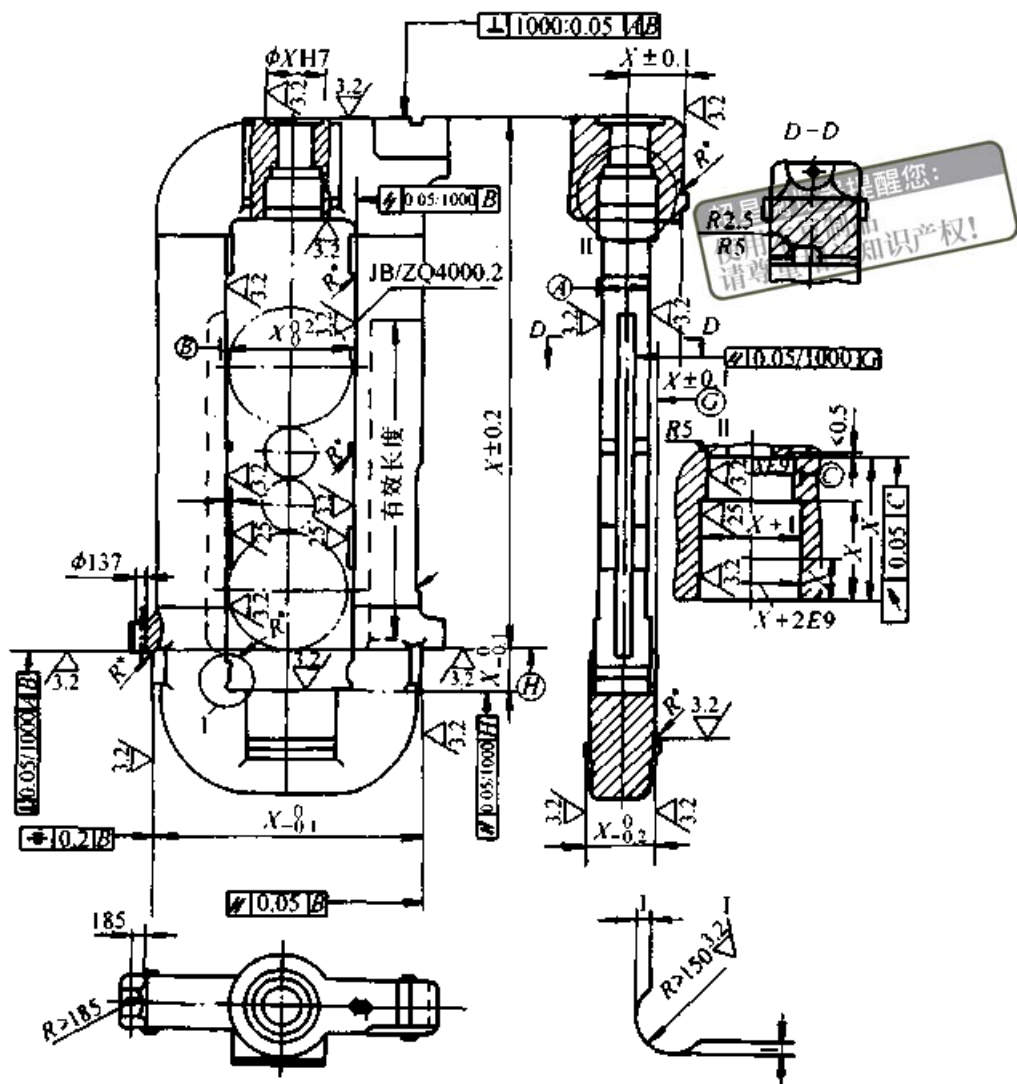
四辊轧机机架形位公差和尺寸公差
